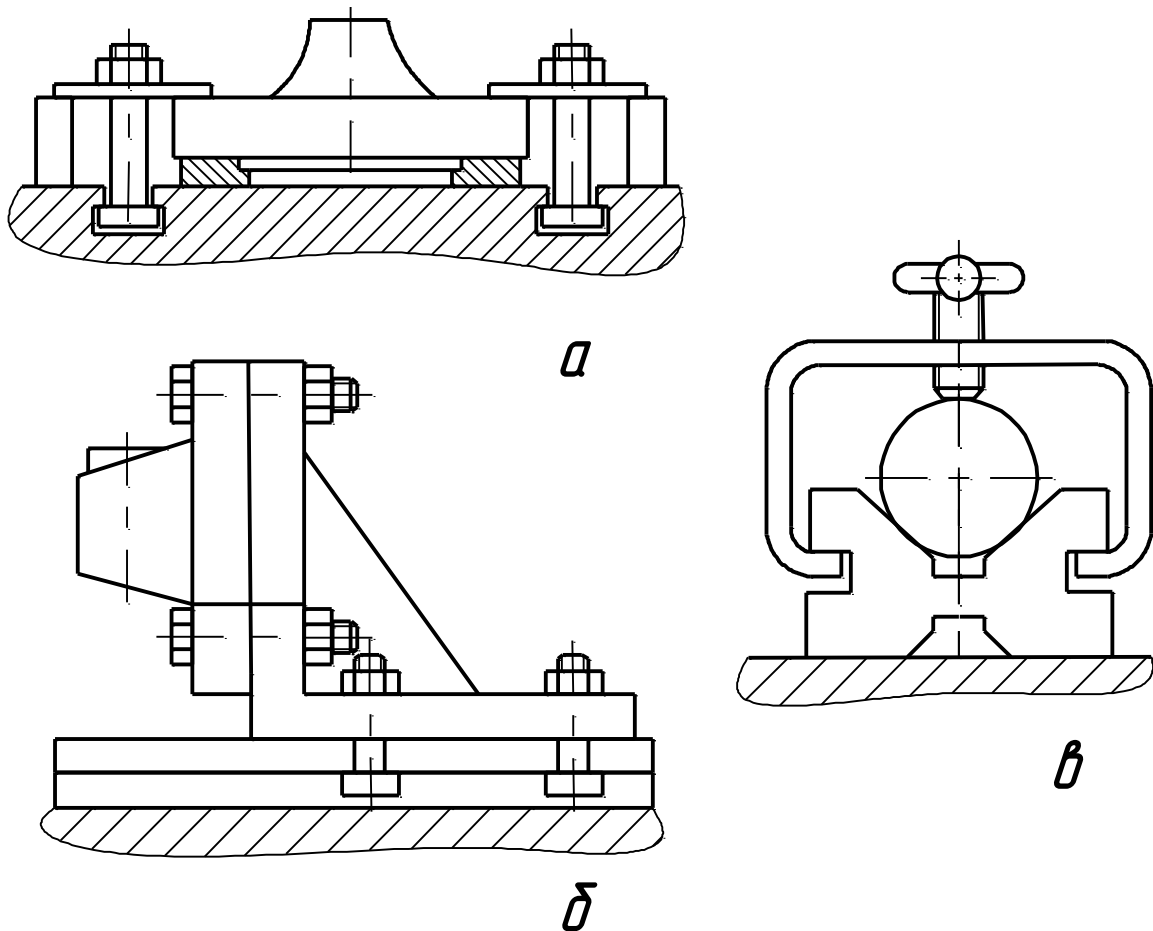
Способи закріплення заготовок на свердлильних верстатах
